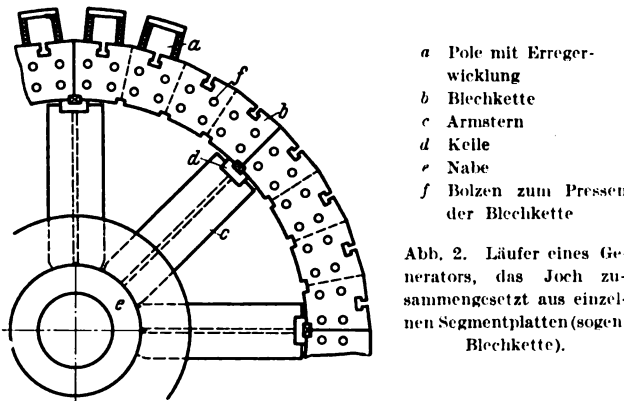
Läufer eines Generators, das Joch zusammengesetzt aus einzelnen Segmentplatten (sogen. Blechkette).
